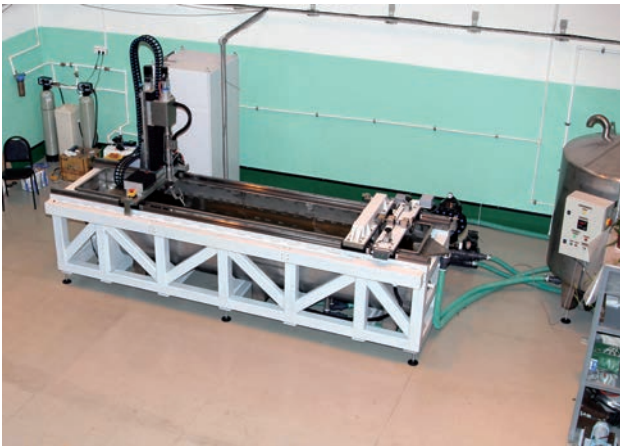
Установка АСНК-ВАЛ для контроля заготовок валов авиационных двигателей. АО «ПМЗ»
